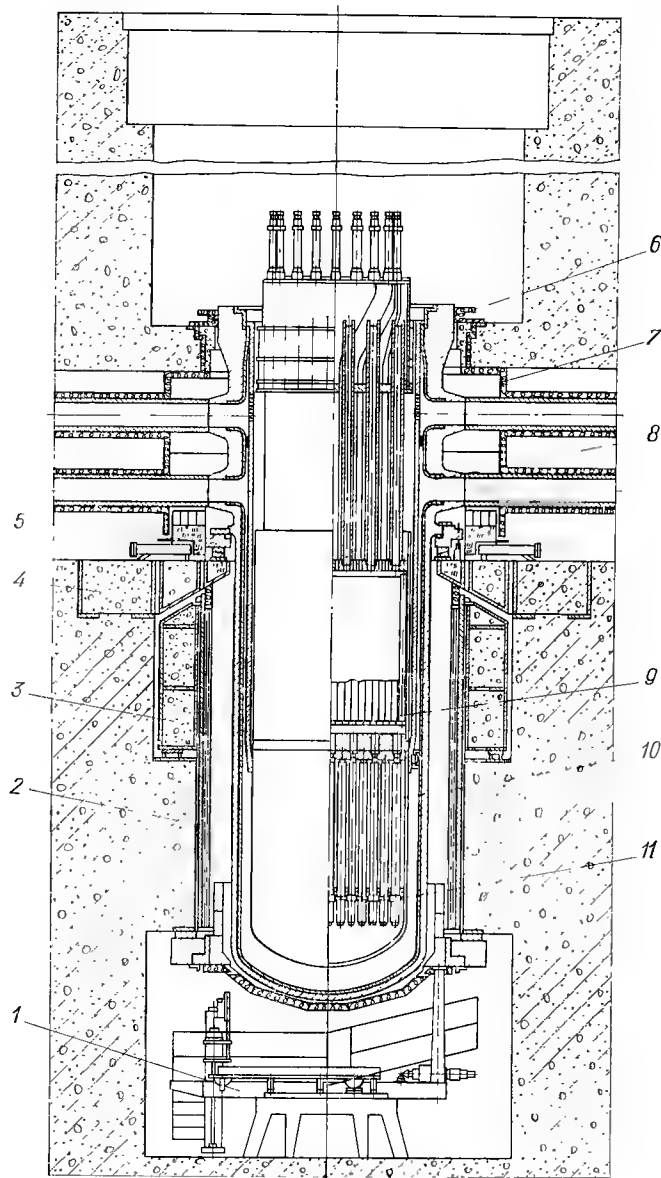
Установка внутрикорпусных устройств ВВЭР-440.
